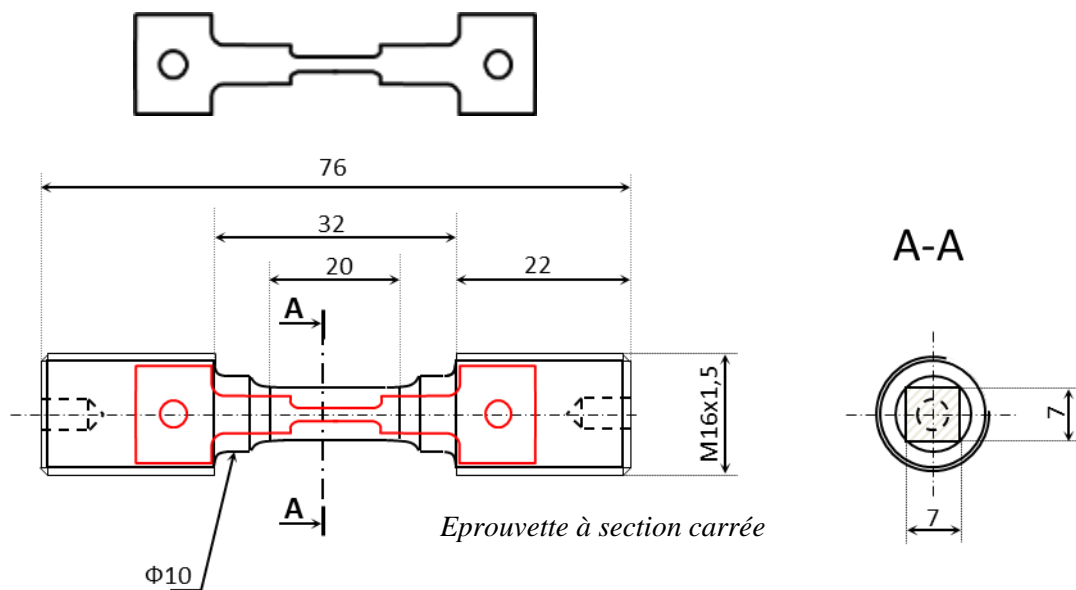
Dimensions des éprouvettes à section carrée et microéprouvettes longues
